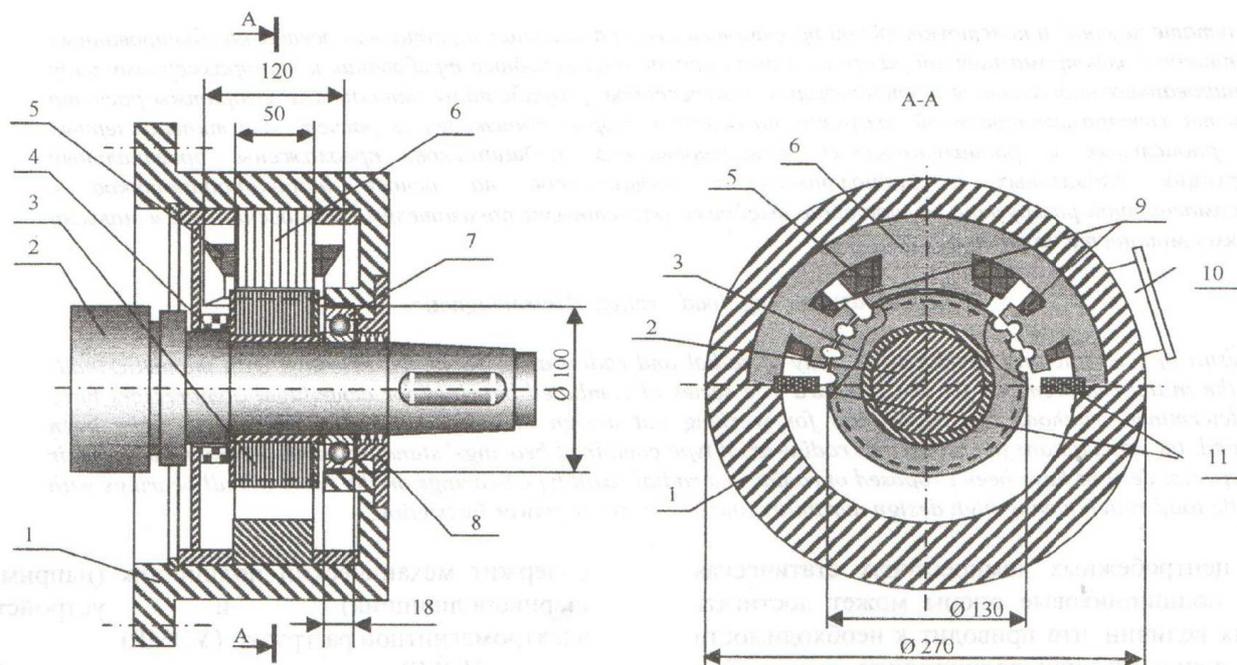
Компоновка радиального подшипника первого типа: 1 – корпус подшипника; 2 – вал компрессора; 3 – ротор устройства электромагнитной разгрузки (УЭМР); 4 – датчик положения вала компрессора; 5 – обмотка возбуждения статора УЭМР; 6 – магнитопровод статора УЭМР; 7 – шарикоподшипник; 8 – лабиринтная втулка; 9 – генераторные обмотки; 10 – коробка для электрорадиоэлементов; 11 – постоянные магниты
